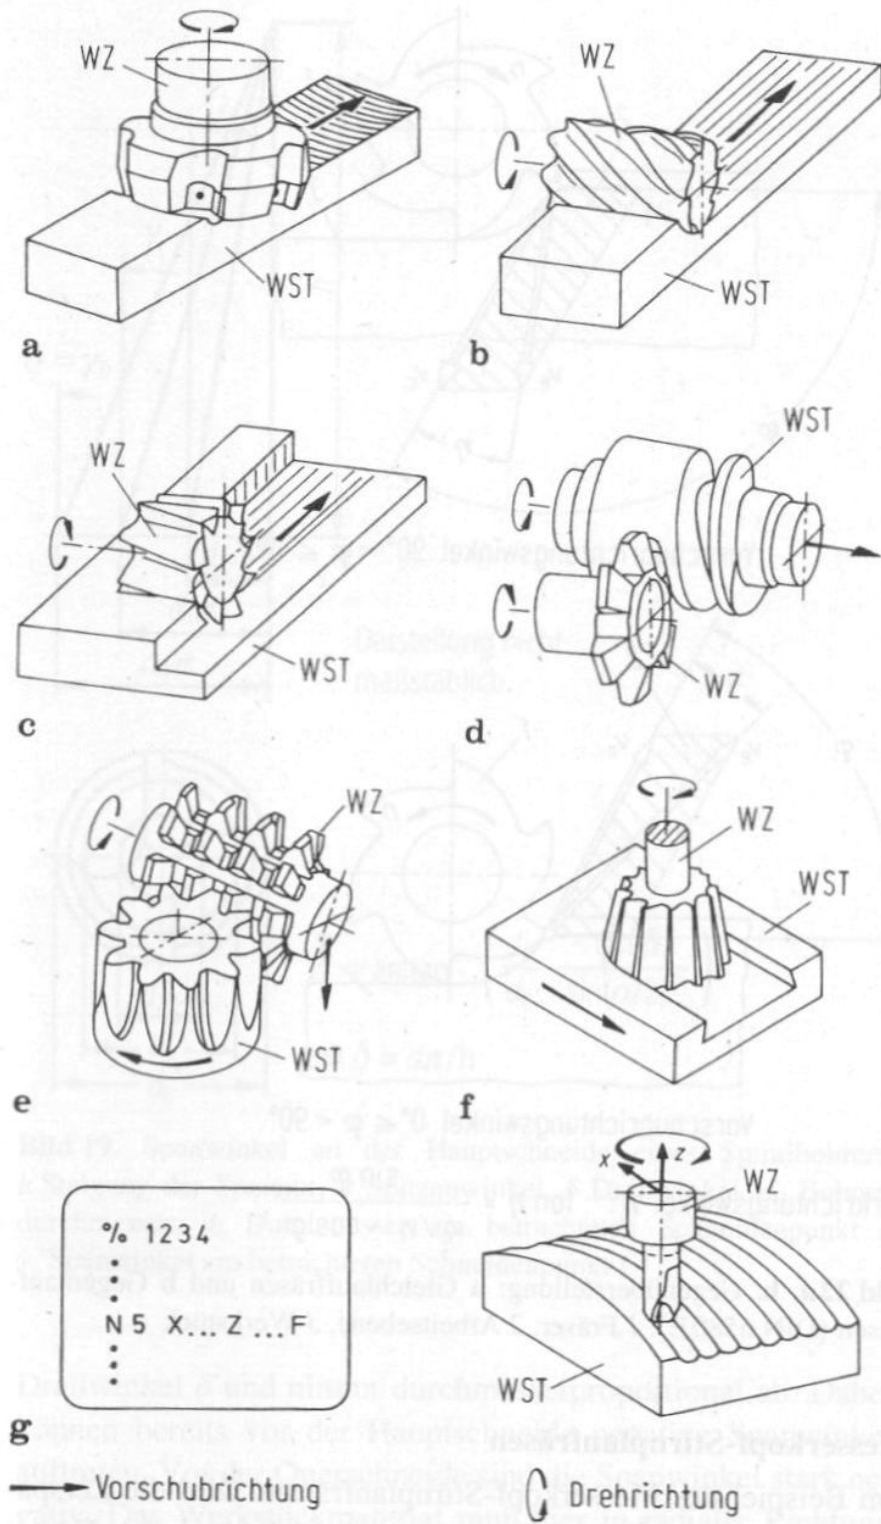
a-g. Fräsverfahren (DIN 8589). Planfräsen: a Stirnfräsen; b Umfangsfräsen; c Umfangs-Stirnfräsen; d Schraubfräsen; e Wälzfräsen; f Profilfräsen; g Formfräsen: WST - Werkstück, WZ - Werkzeug
